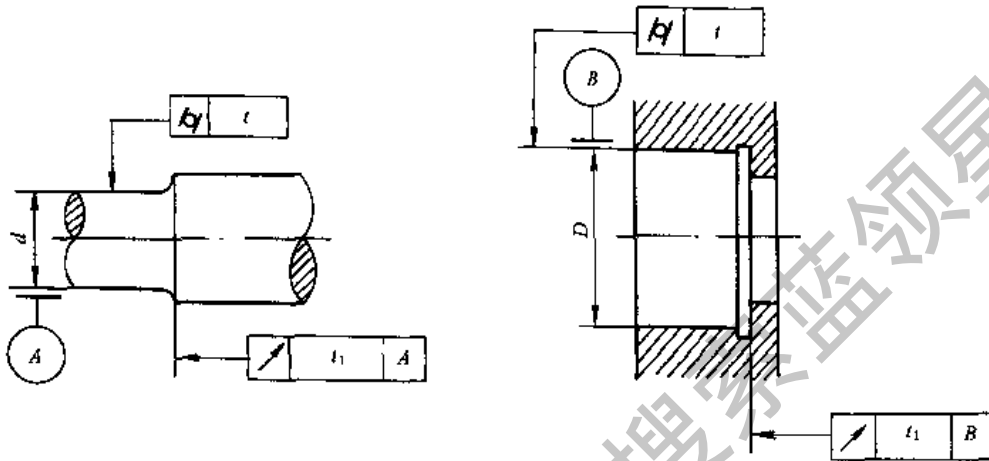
轴与外壳配合表面及端面的形位公差
